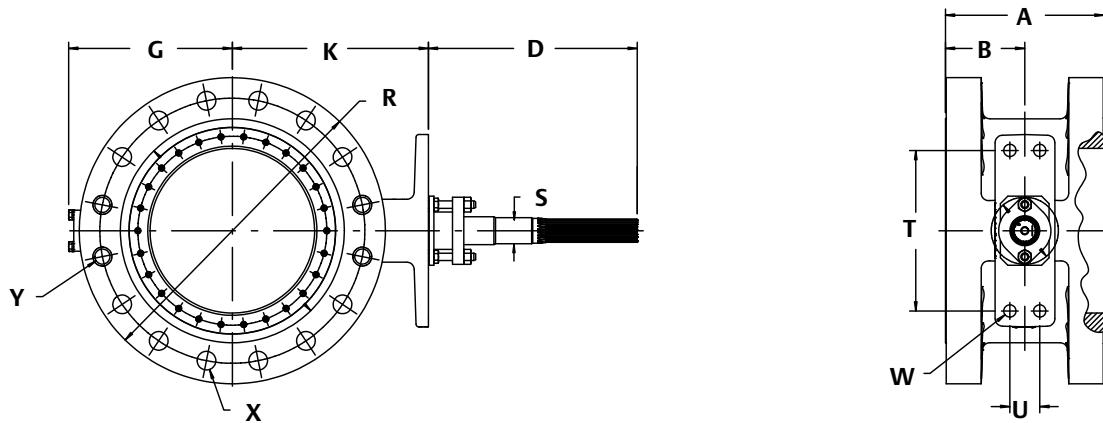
Размеры затвора 8532 в двухфланцевом корпусе
